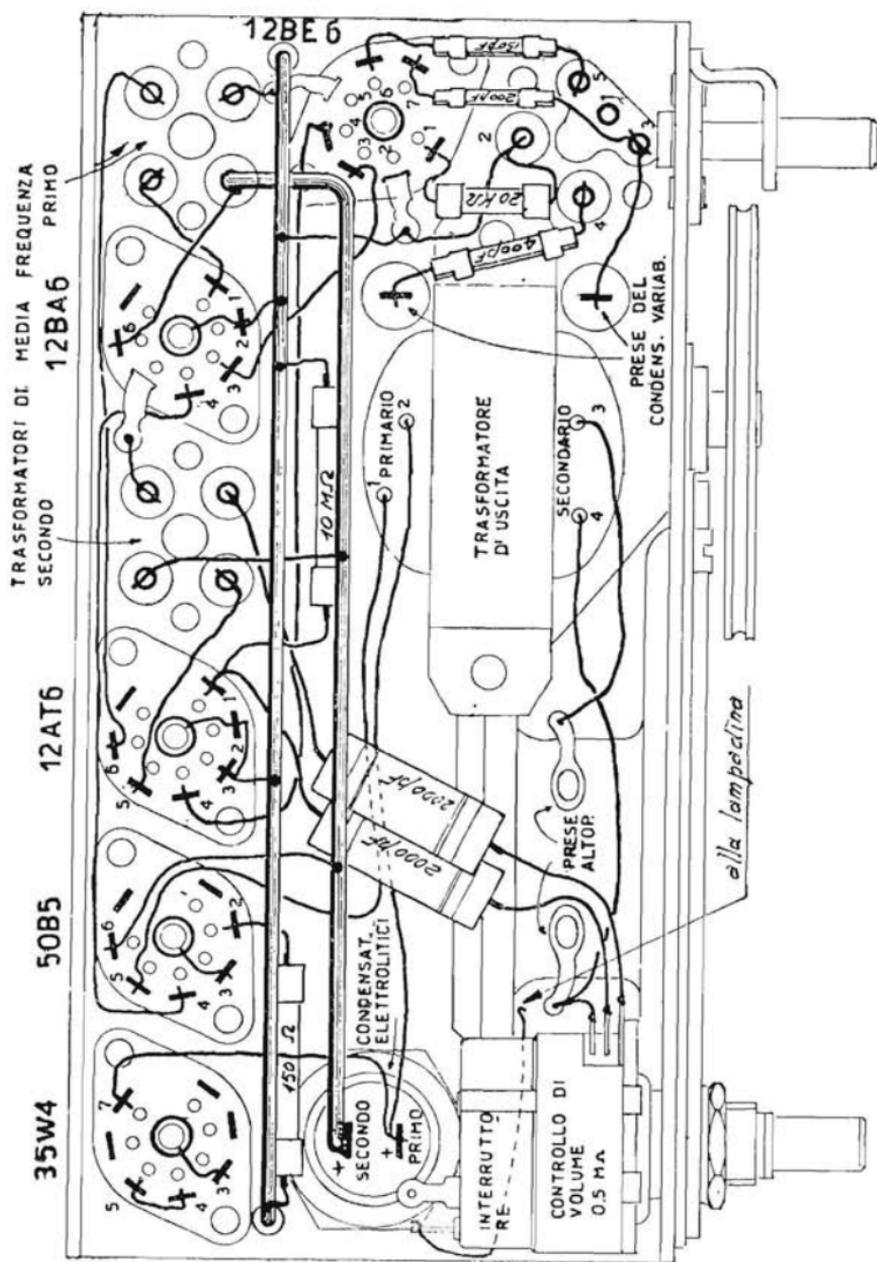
Prima fase del montaggio sotto il telaio.
